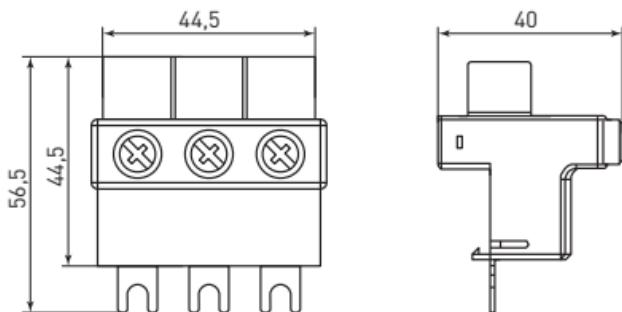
Габаритные размеры соединительного блока АПД/GV2
